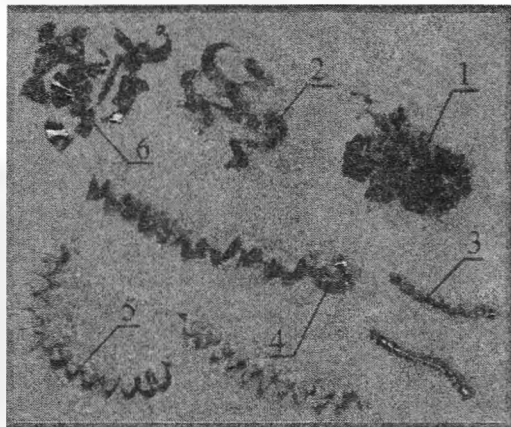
Формы стружки при сверлении сплава Ti6Al4V-ELI
